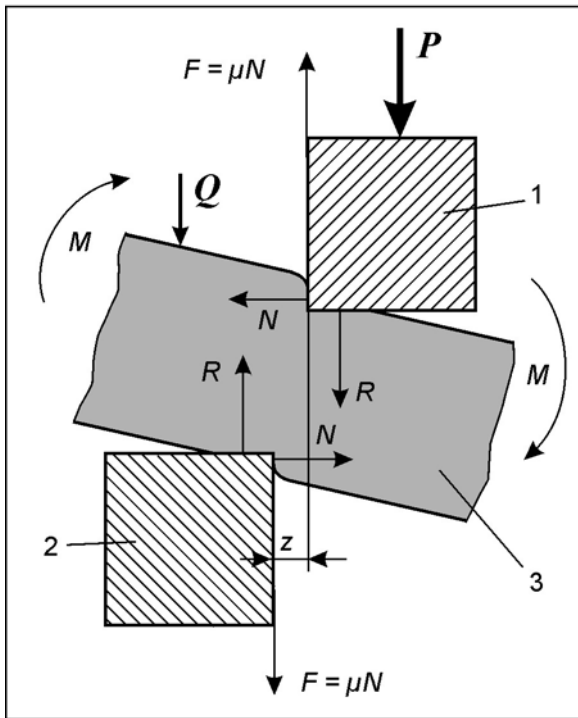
Схема дії сил при відрізуванні: 1 – ніж рухомий; 2 – ніж нерухомий; 3 – заготовка
